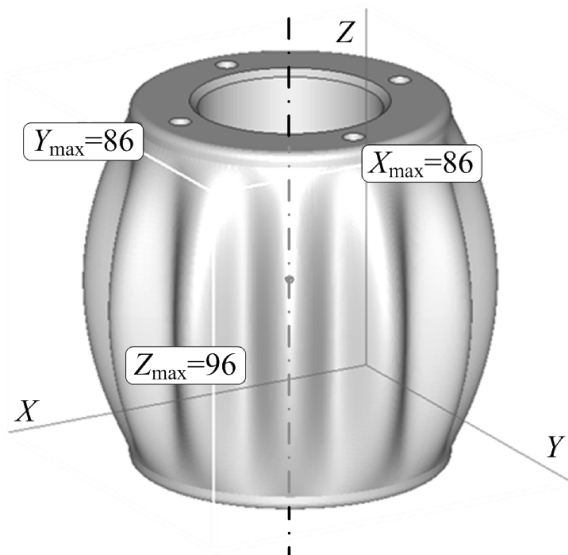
3D-компьютерная модель корпуса гидроакустического преобразователя продольно-изгибного типа с волнообразной излучающей поверхностью
